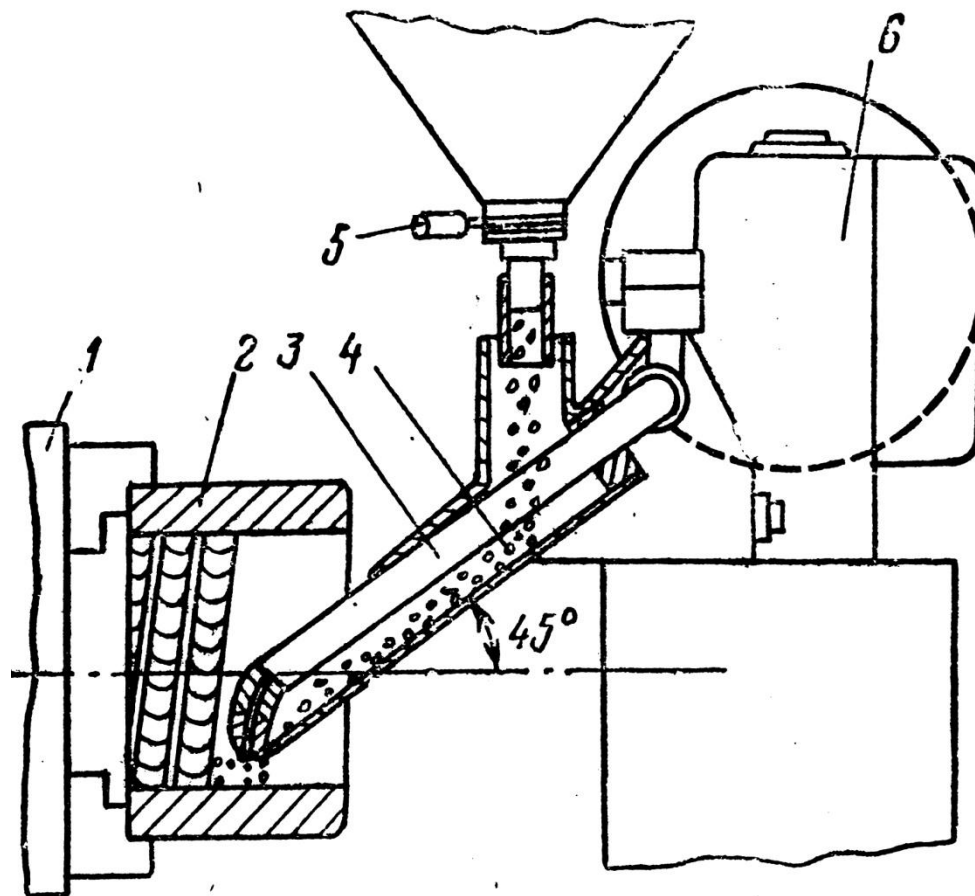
Схема наплавки под слоем флюса поверхности отверстия:
